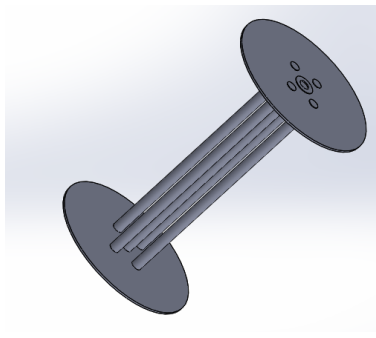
Carrete de almacenamiento del alambre Diseño 3D en SolidWorks
